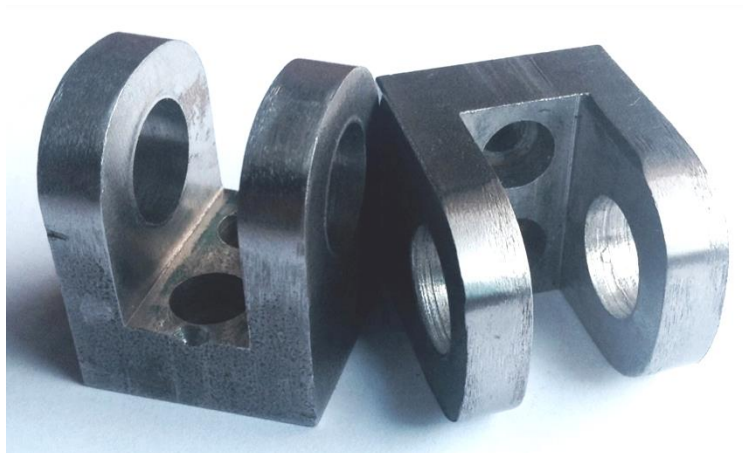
Macho-oreja, pieza que se ensambla a la placa base y contendrá a la "oreja".
